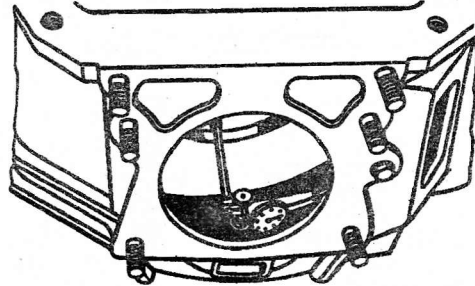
Проверка concentricity отверстия картера сцепления с осью коленчатого вала приспособлением 24-У-114625
